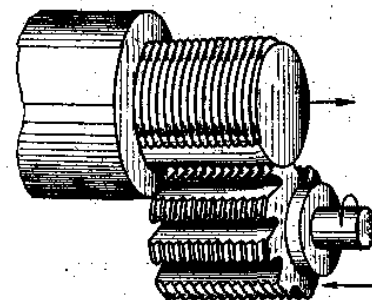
Фрезерование резьбы гребенчатой фрезой
